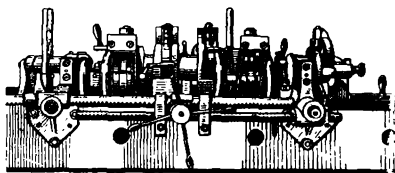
Контрольное приспособление для измерения фактического припуска на шатунных шейках в поковке коленчатого вала шестицилиндрового автомобильного двигателя по схеме, показанной на рис. 41
